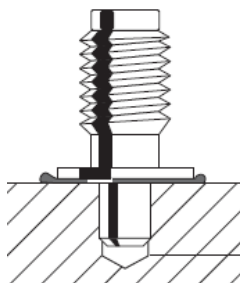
Устройство шпильки, установленной без сквозного сверления
